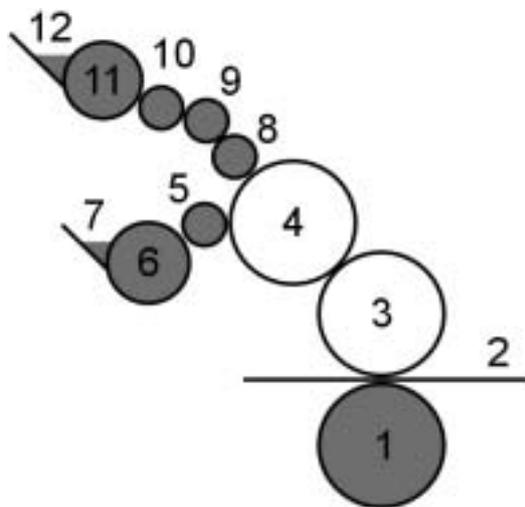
Схема печатного аппарата машины для офсетной печати: 1 — печатный цилиндр; 2 — запечатываемый материал; 3 — офсетный цилиндр; 4 — формный цилиндр; 5 — накатной увлажняющий валик; 6 — увлажняющий валик; 7 — подача увлажняющего раствора; 8 — накатной красочный валик; 9 — раскатной валик; 10 — передающий валик; 11 — дукторный валик; 12 — красочный резервуар
